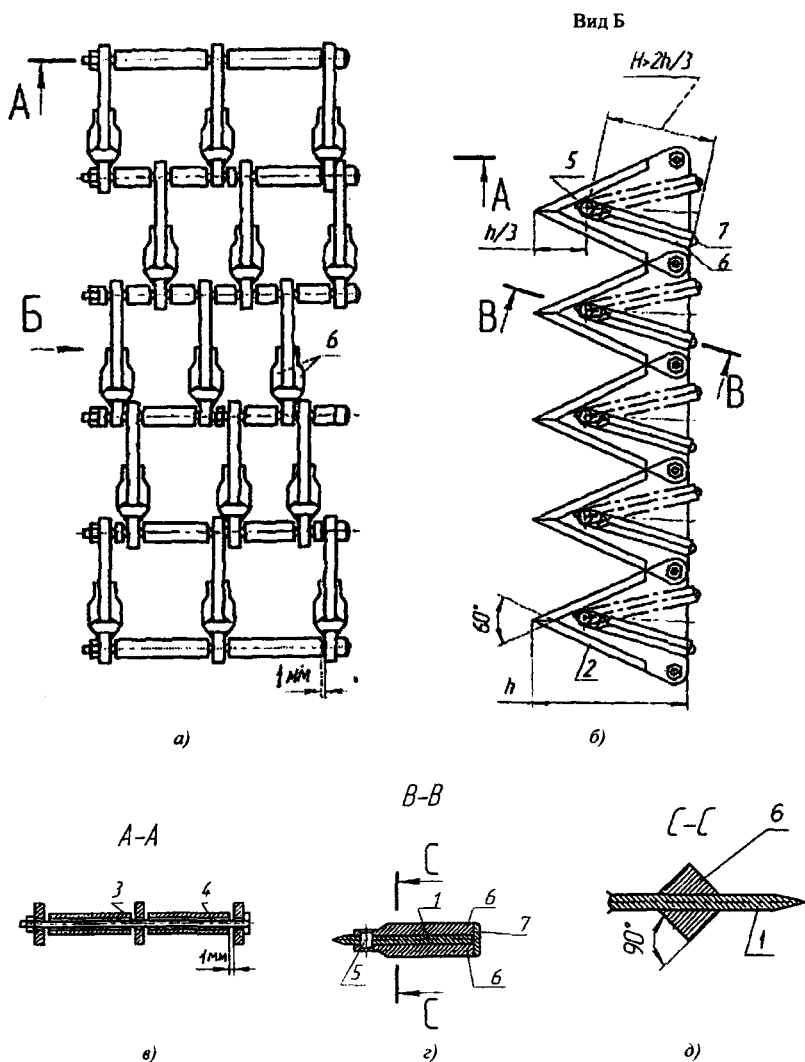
Борона гибкая для глубокого рыхления почвы:
